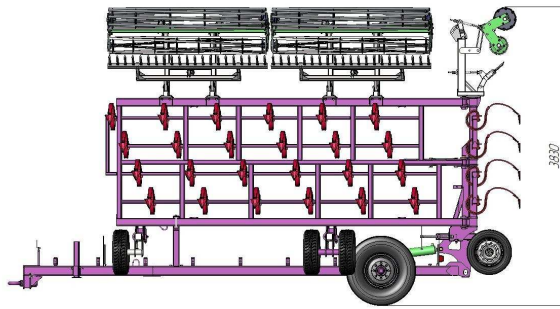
Общий вид культиватора Кусто-12М. 1- основная рама; 2-левое крыло; 3-правое крыло; 4-дышло; 5-инструментальная рама; 6 -разрыхлитель; 7 -каток прикатывающий; 8 -транспортное колесо; 9 -технологические колеса; 10 -регулирующий винт
